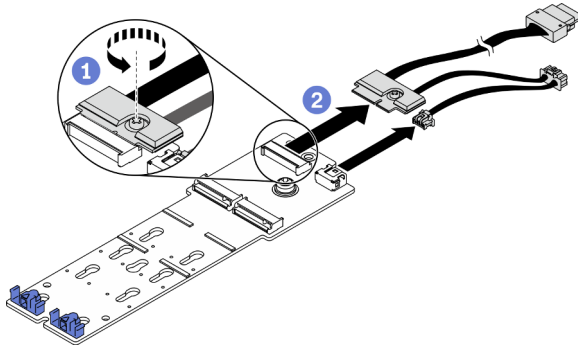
Débranchement des câbles de fond de panier M.2 du fond de panier M.2
